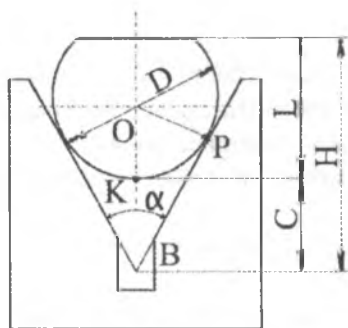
Схема установки заготовки в призме при фрезеровании лыски
